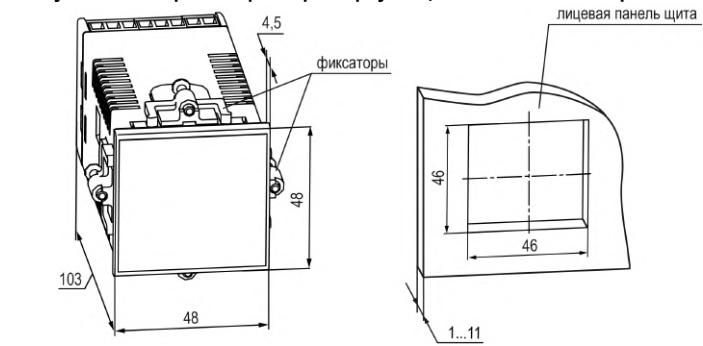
Габаритные размеры корпуса Щ5 и монтажного отверстия в щите
